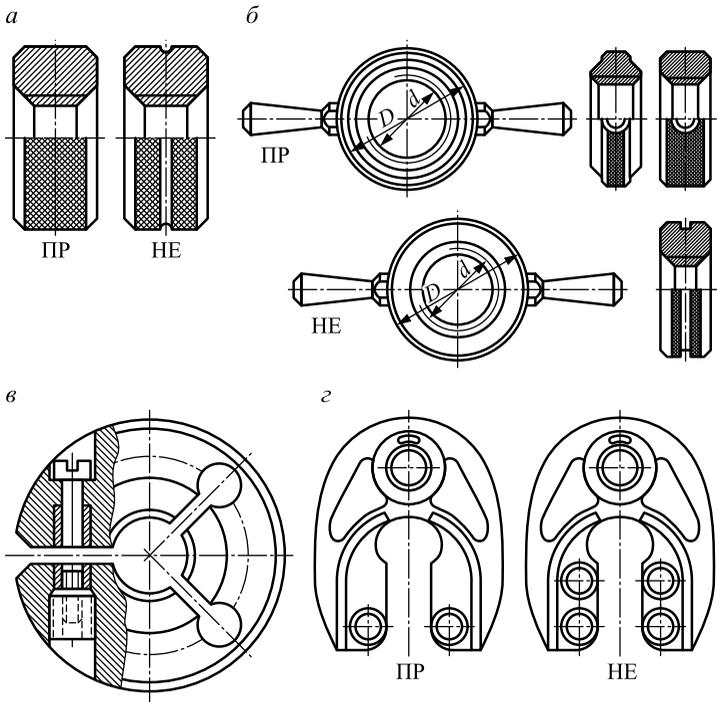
Резьбовые калибры-кольца и калибры-скобы:
